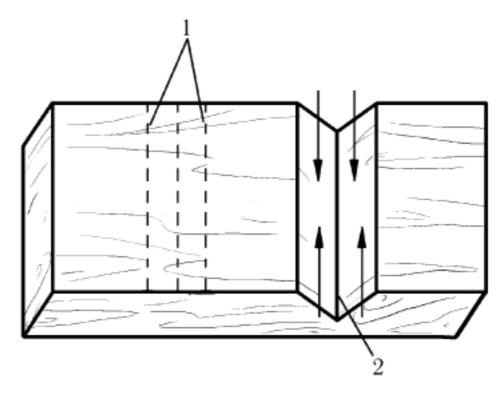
Выполнение прямой двусторонней выемки поперек волокон заготовки (стрел-ками указано направление движения ножа): I – разметка; 2 – средняя линия
